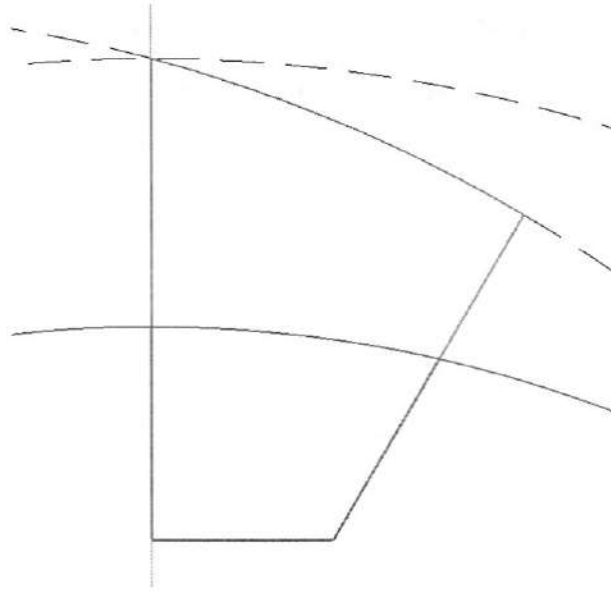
Робоче положення рейки черв'ячної фрези
